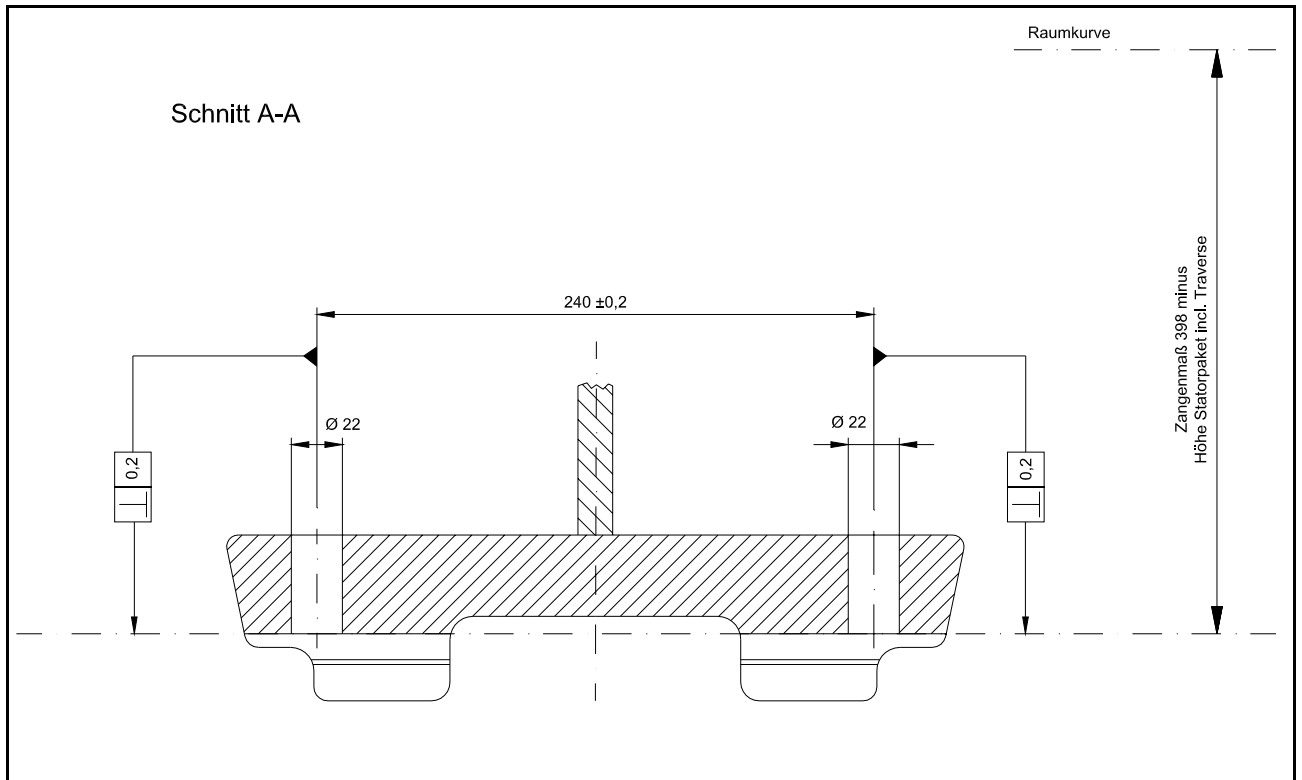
Maße und Toleranzen für die Ausführung der Statorpaketaufnahme in Stahlbauweise (Querschnitt)
